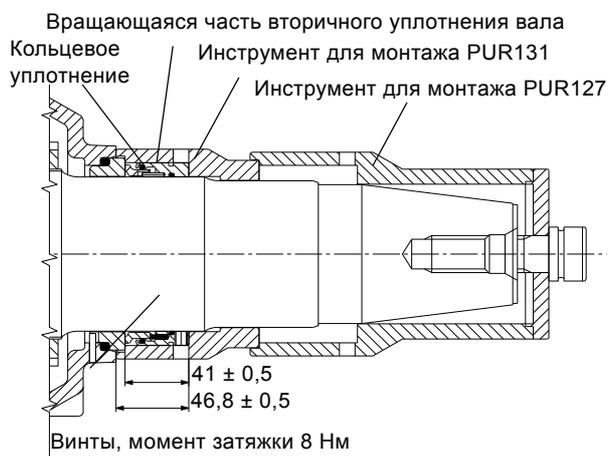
Установка вращающейся части вторичного уплотнения вала, типоразмер 74
